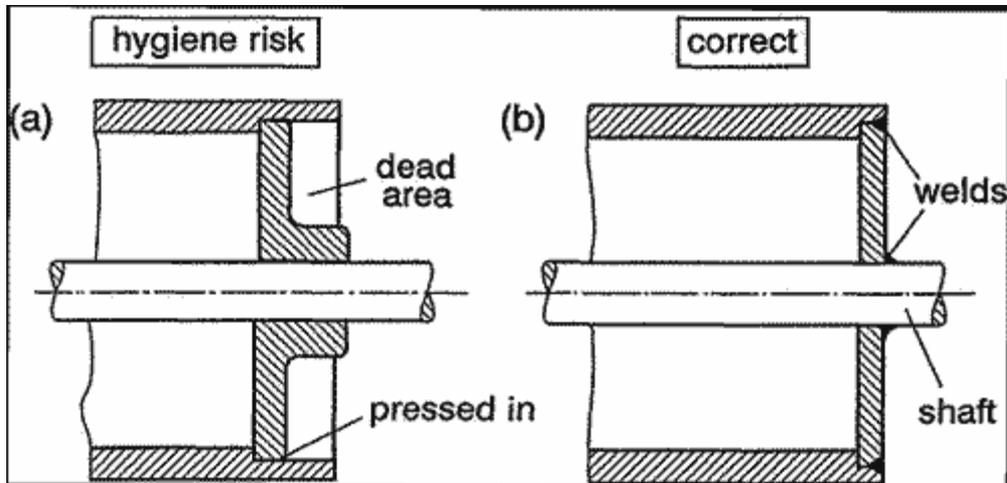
Конструкция барабанов. (а) углубления на боковых поверхностях барабанов образуют «мертвые зоны» скопления продукта; (б) сплошные сварные боковые поверхности, предотвращают возможность возникновения гигиенического риска и легко очищаются.
